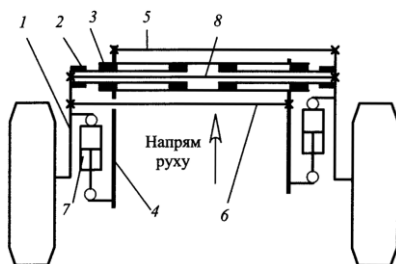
Схема задньої підвіски на поздовжніх важелях з широкою опорною базою: 1 — поздовжній важіль; 2 — пружина; 3 — амортизатор з буфером віддачі; 4 — буфер стискування; 5 — кузов
